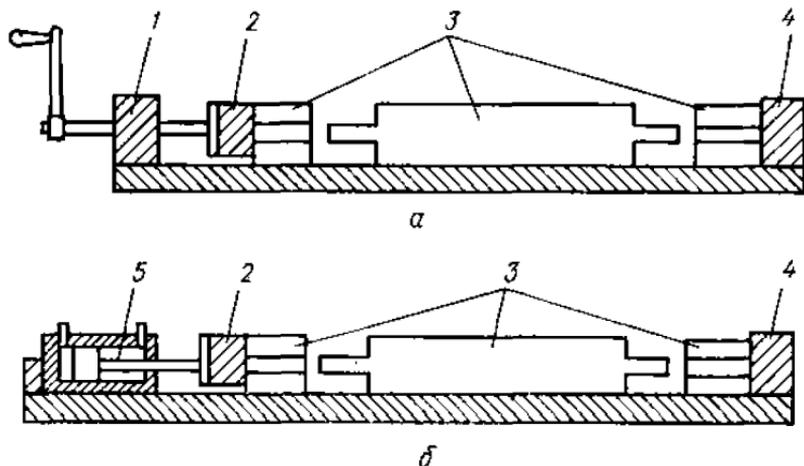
Схемы механизмов сжатия в сборочных станках:
